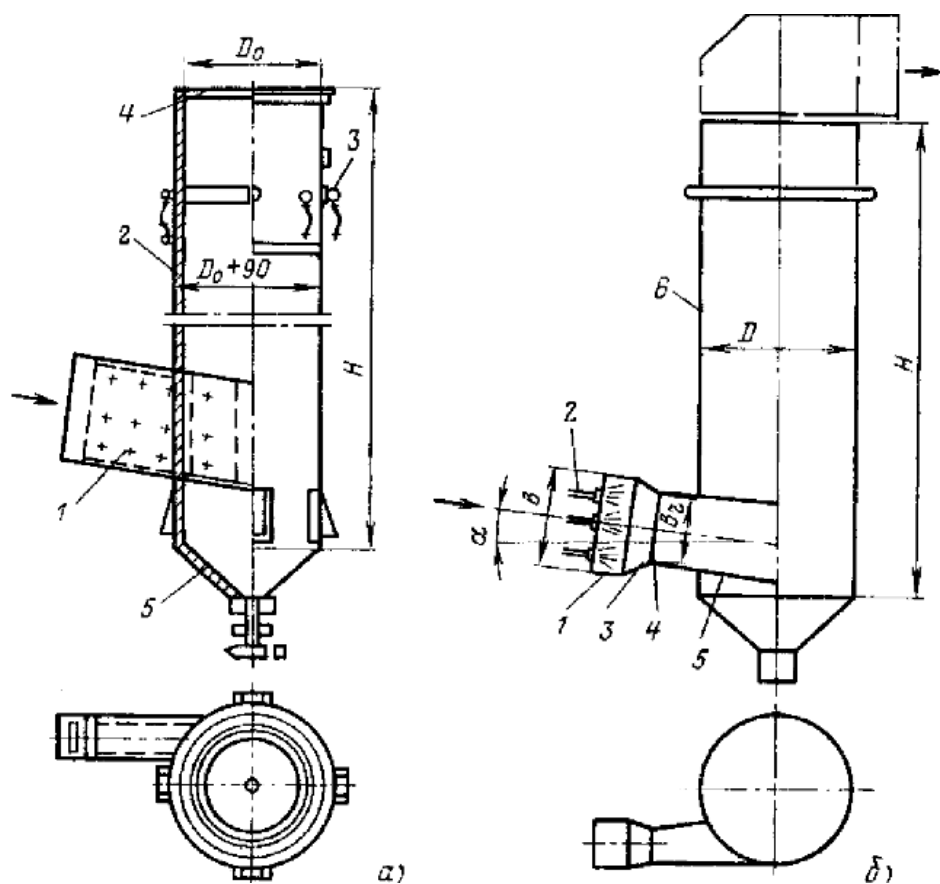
Мокрые золоуловители: а - центробежный скруббер; 1 - входной патрубок запыленного газа; 2 - корпус золоуловителя; 3 - оросительные сопла; 4 - выход очищенного газа; 5 - бункер; б - золоуловитель с коагулятором Вентури; 1 - входной патрубок запыленного газа; 2 - подача воды через оросительные сопла; 3, 4, 5 -конфузор, горловина и диффузор коагулятора Вентури; 6 - скруббер-каплеуловитель
